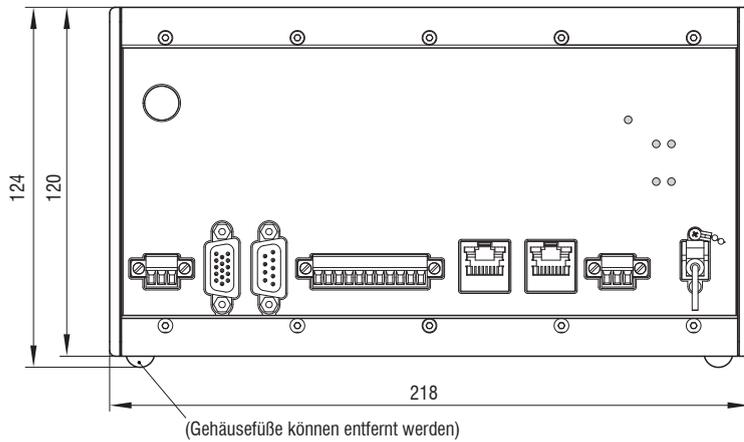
Maßzeichnung Frontansicht des IMC5420 Controllers, Abmessungen in mm (Zoll)
